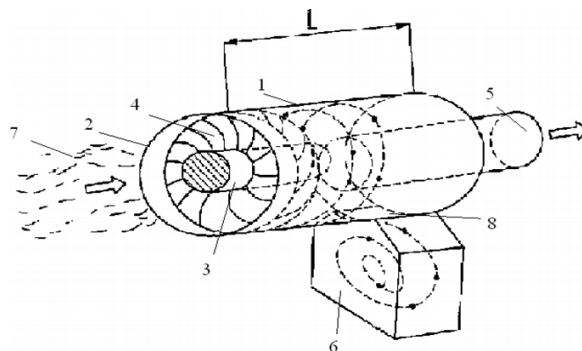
Схема фільтра для очищення рідини за патентом США [9]: 1 – циліндричний корпус; 2 – вхідний патрубок; 3 – внутрішній циліндричний корпус; 4 – нерухомий лопатевий закручувальний апарат; 5 – вихідний патрубок; 6 – грязьозбірник; 7 – потік забрудненої рідини; 8 – щілина для відведення твердих частинок забруднень з потоку рідини
